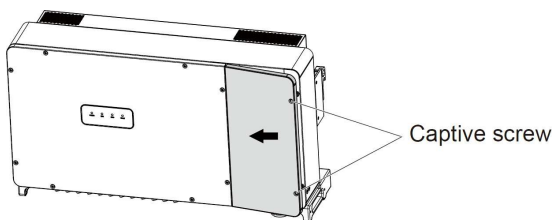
Abra la cubierta superior de la caja combinadora
